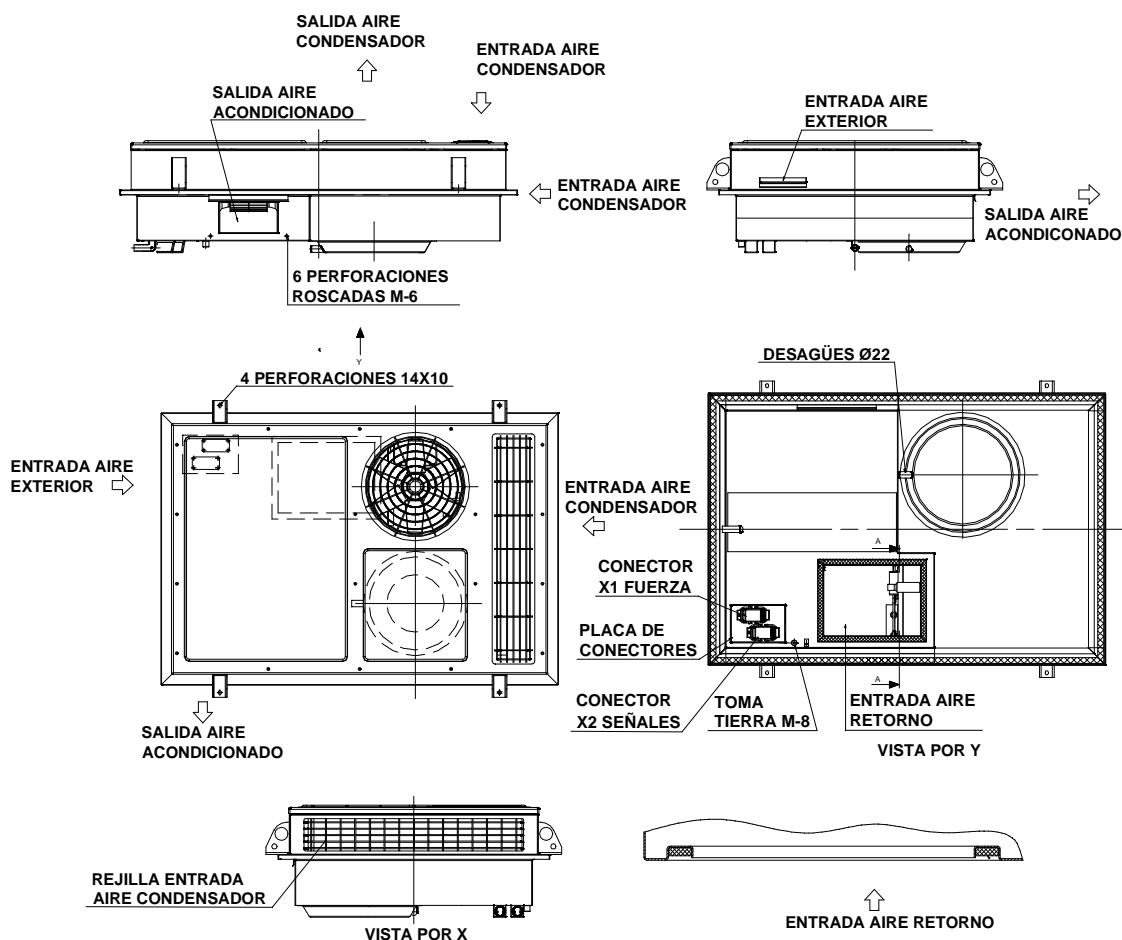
Desmontaje y montaje del equipo de aire acondicionado de cabina
